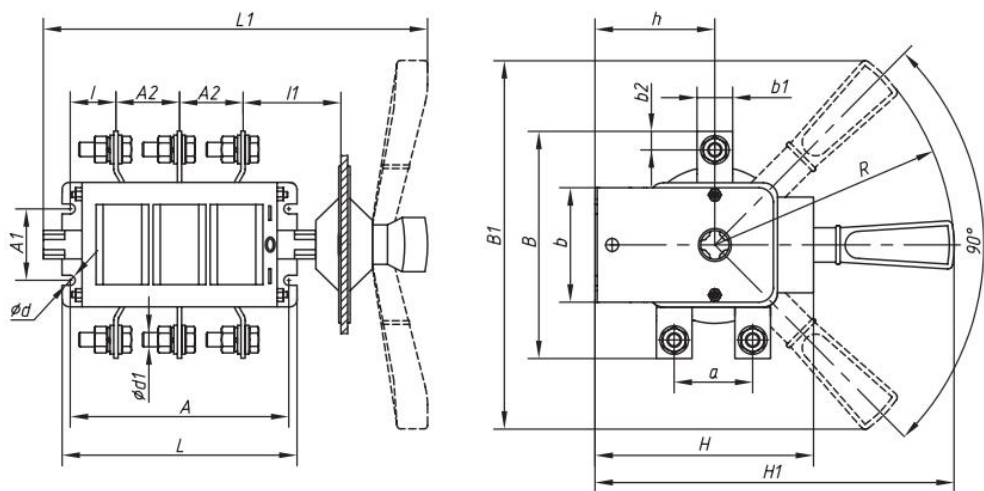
Выключатель-разъединитель универсальный трехполюсный на два направления с д/г камерами, съемная левая/правая рукоятка
